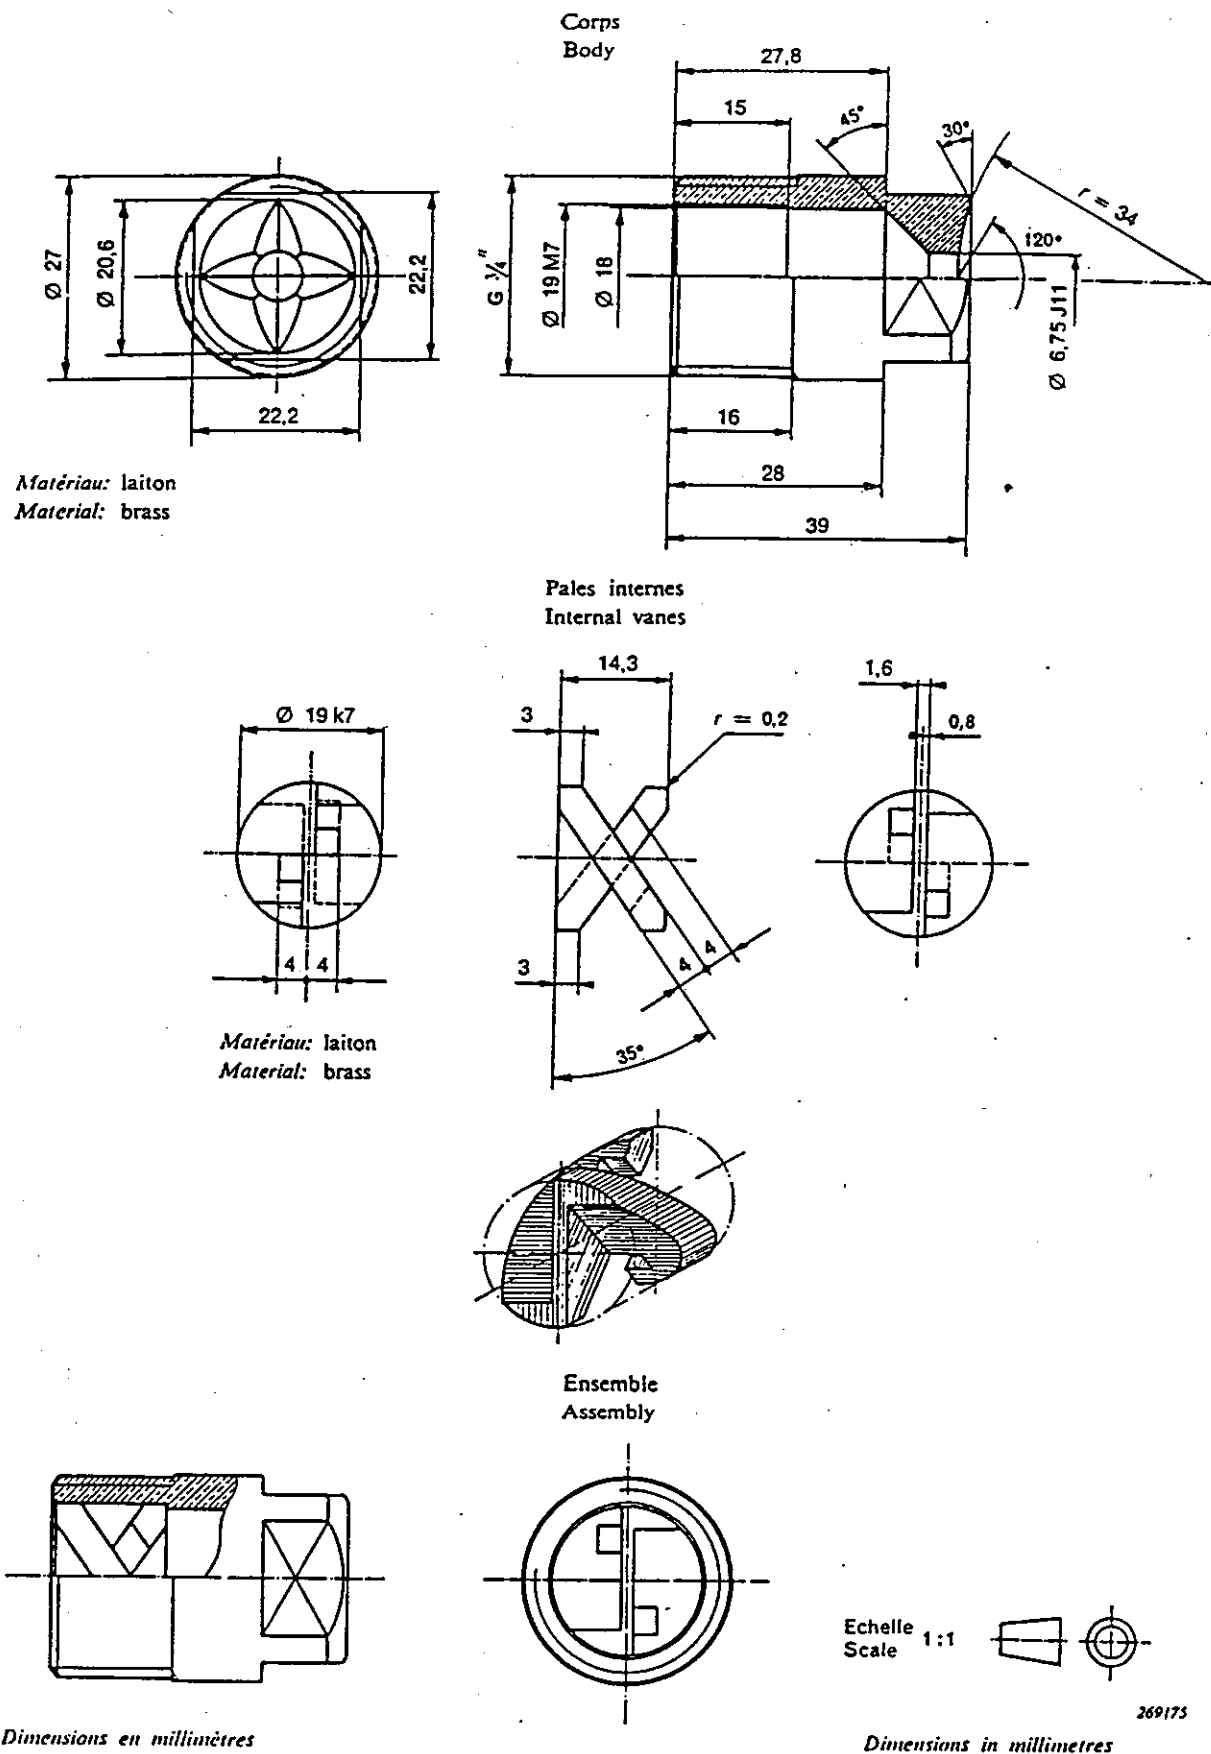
Exemple d'une lance répondant aux exigences de l'essai contre les intempéries
